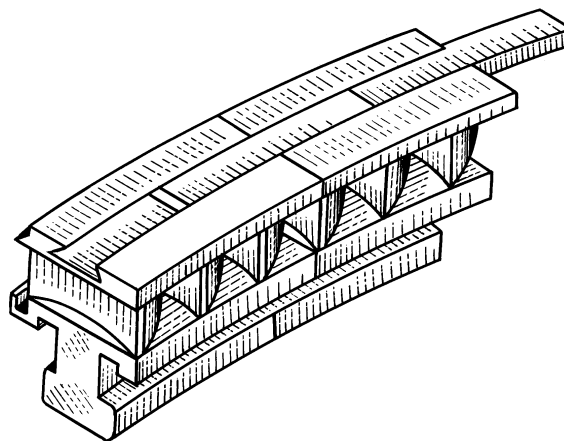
Пакеты рабочих лопаток с демпферной связью для регулирующей ступени ЦВД
